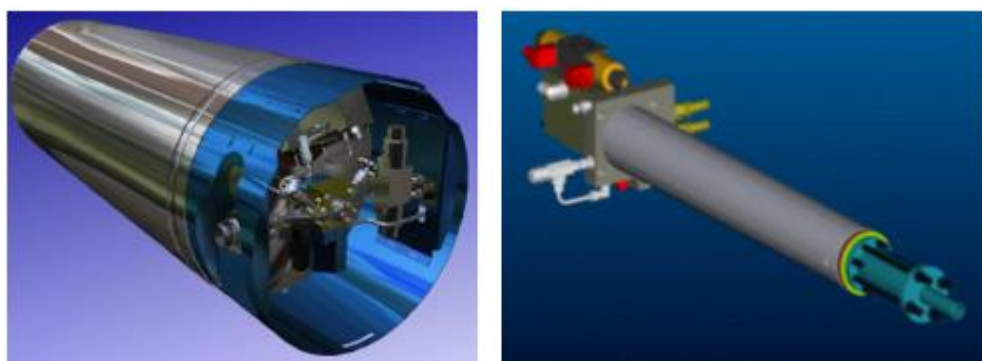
Módulo tanque GNL (izquierda). Bomba y vaporizador de GNL (derecha). Fuente WESTPORT.
